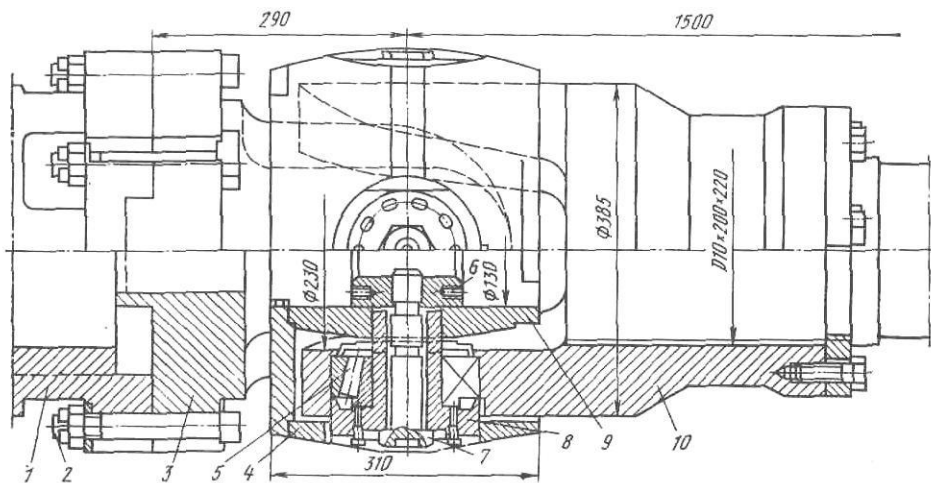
Универсальный шпindelъ с шарнирами на подшипниках качения дрессировочного стана 500/1500×2500
